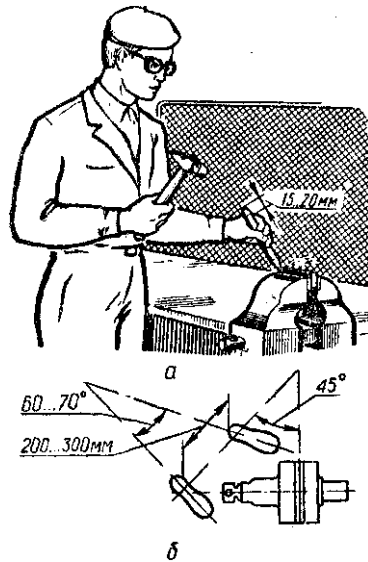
Положення корпуса (а) і ніг (б) під час рубання
